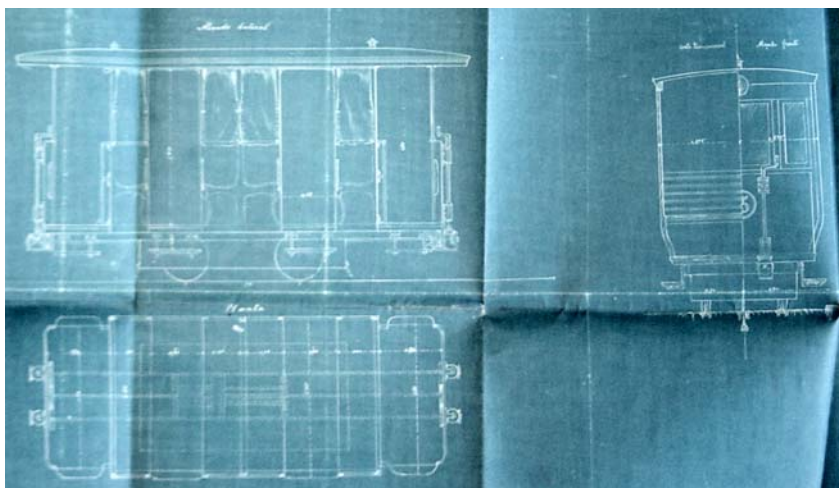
O carro projectado em 1897, em planta, alçado e corte.
